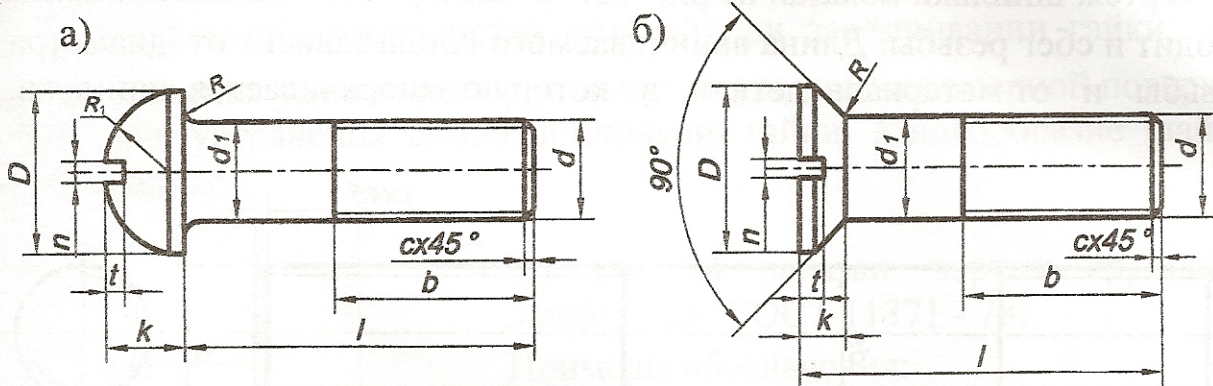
Чертеж винта: а) с полукруглой головкой, б) с потайной головкой; d - номинальный диаметр резьбы; d_1 - диаметр стержня; D - диаметр головки; k - высота головки; R_1 - радиус сферы; R - радиус галтели; t - глубина шлица; p - ширина шлица; l - длина винта; b - длина резьбы.
